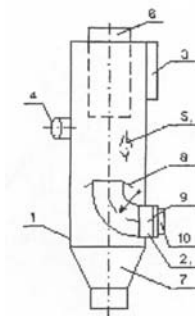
Вихревой коллектор-пылеуловитель конструкции Азарова В.Н., Богуславского Е.И., Мартьянова В.Н.: 1 – цилиндрический корпус; 2 – тангенциальный ввод вторичного потока; 3, 4, 5 – патрубки ввода вторичного потока; 6 – осевой вывод очищенного потока; 7 – конический пылесборник; 8 – осевой ввод первичного потока; 9 – отбойная шайба; 10 – люк для осмотра
